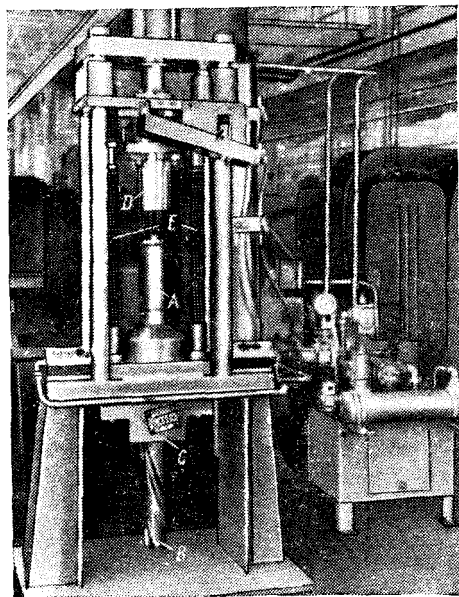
Гидравлический пресс для прошивания зубьев на заготовке колеса
